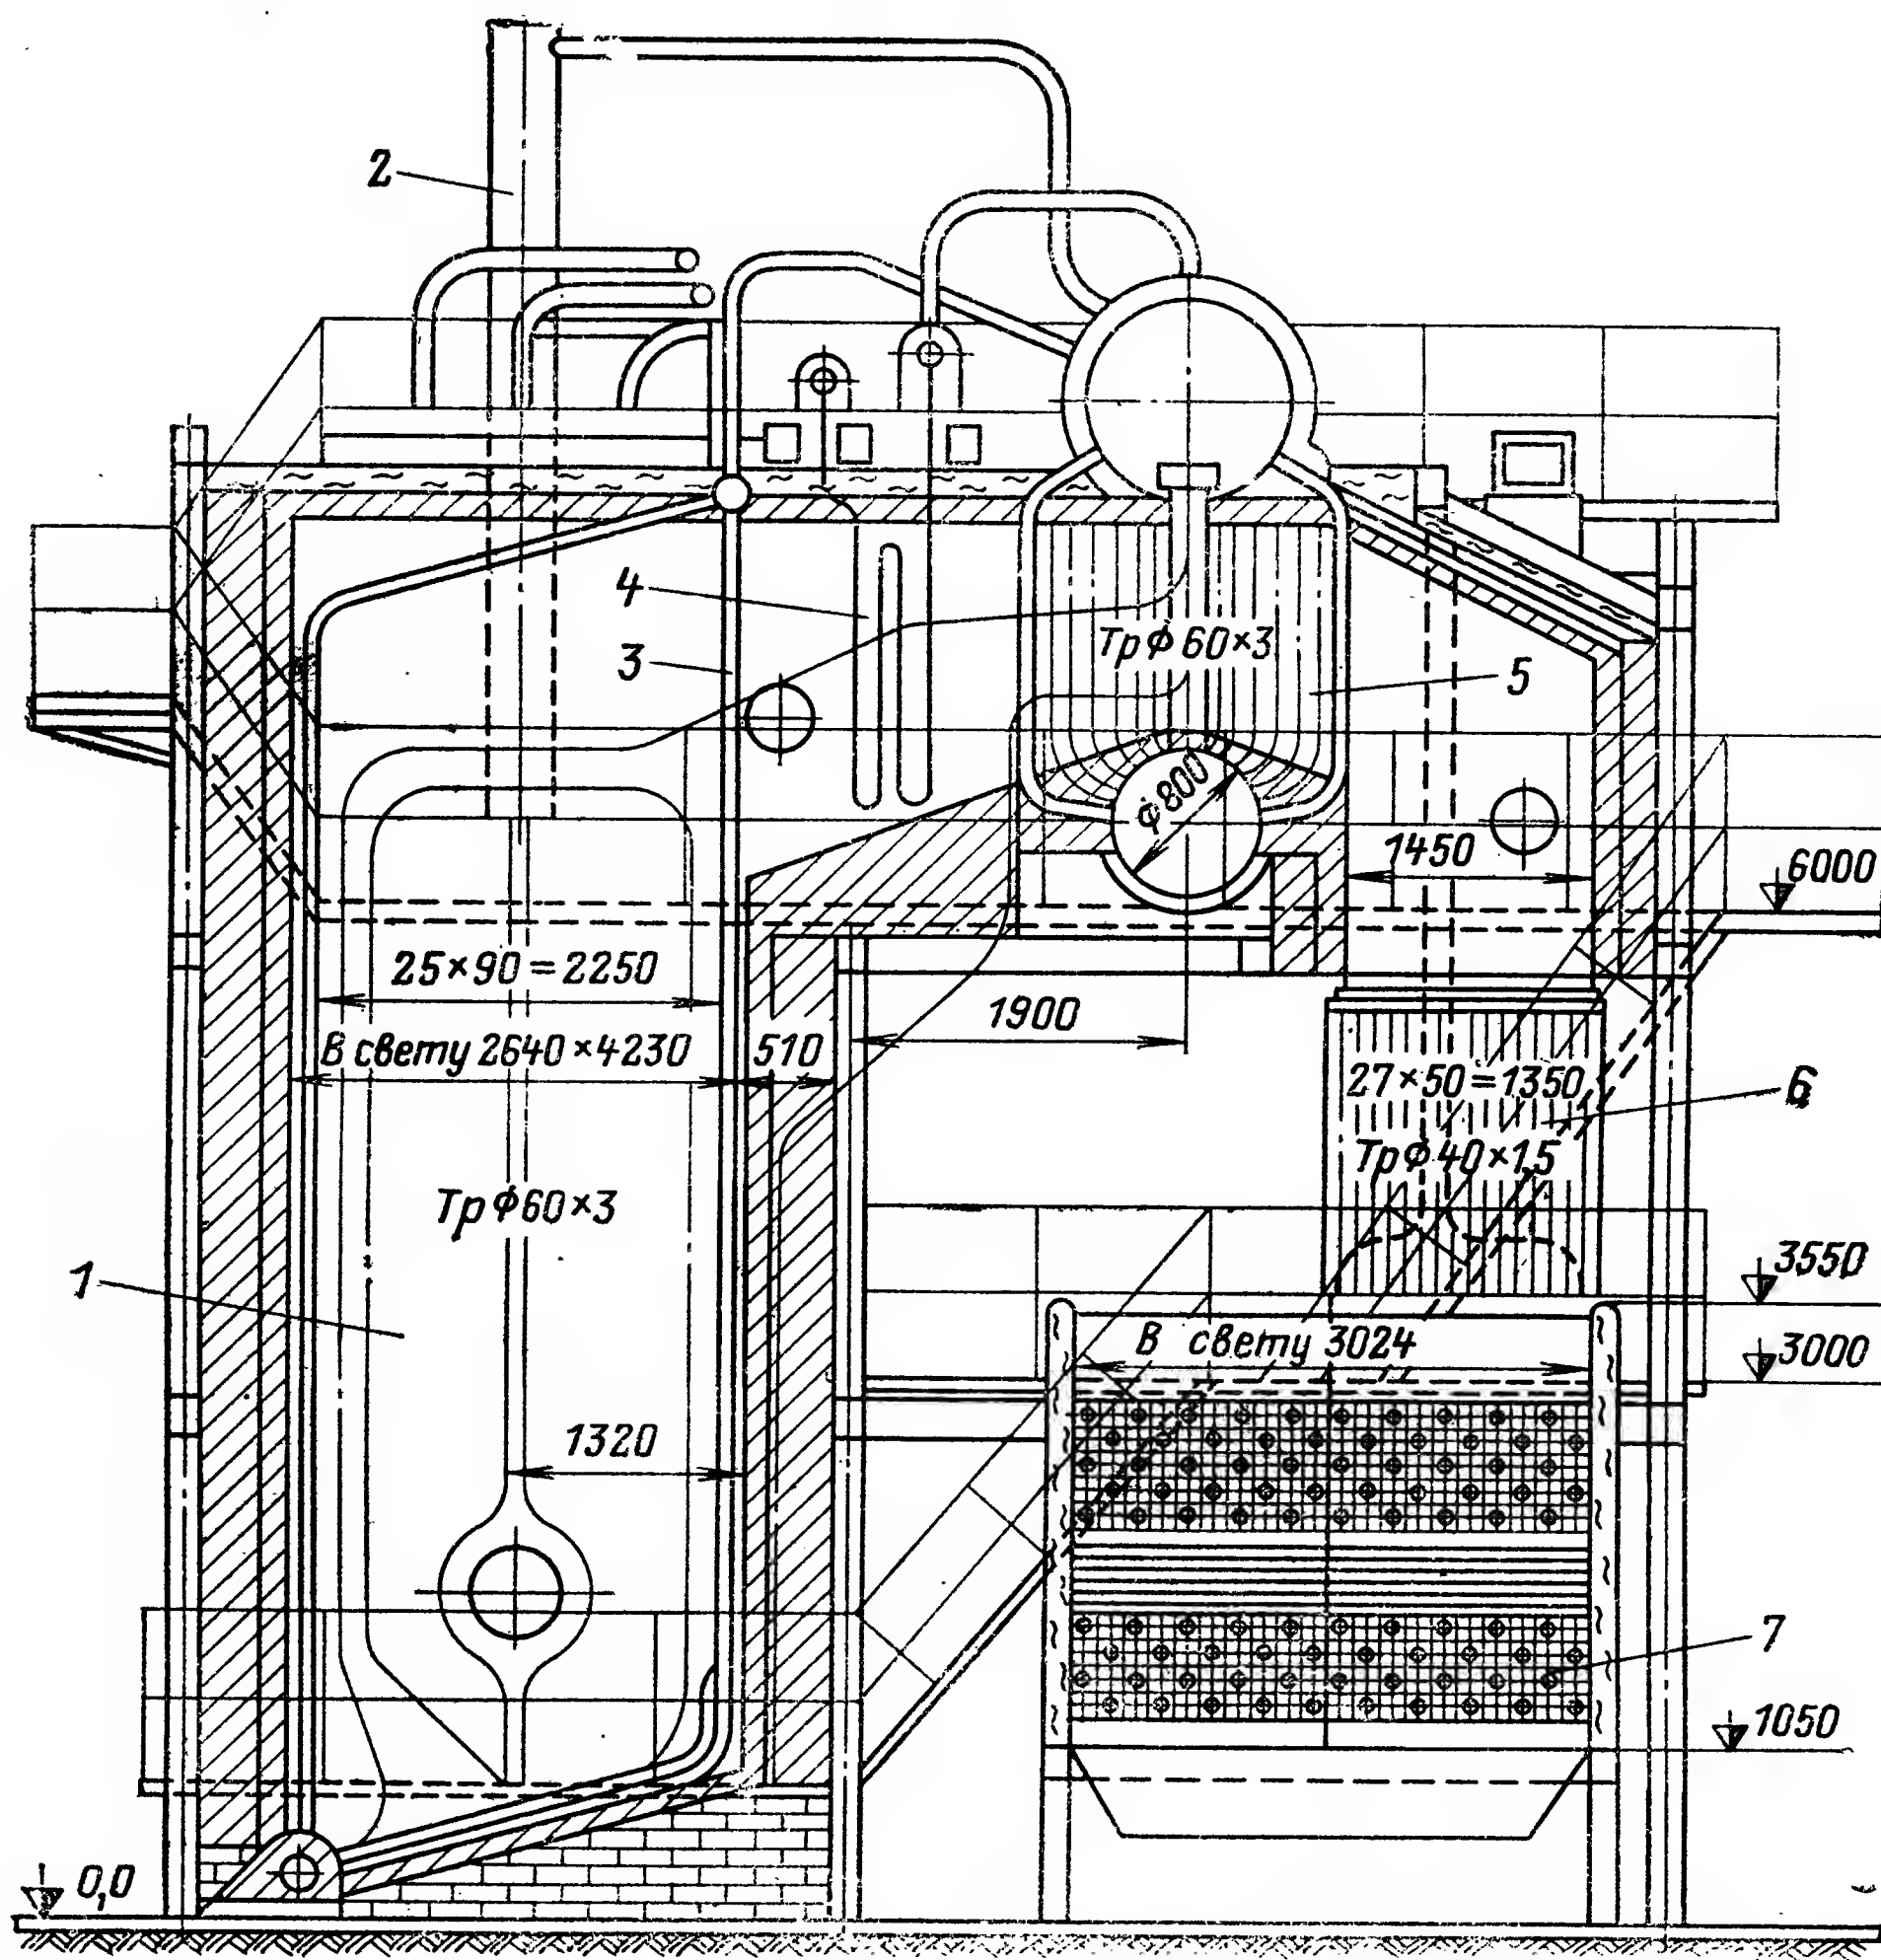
Котлоагрегат Е-25-14 с камерной топкой для сжигания газа и мазута.
